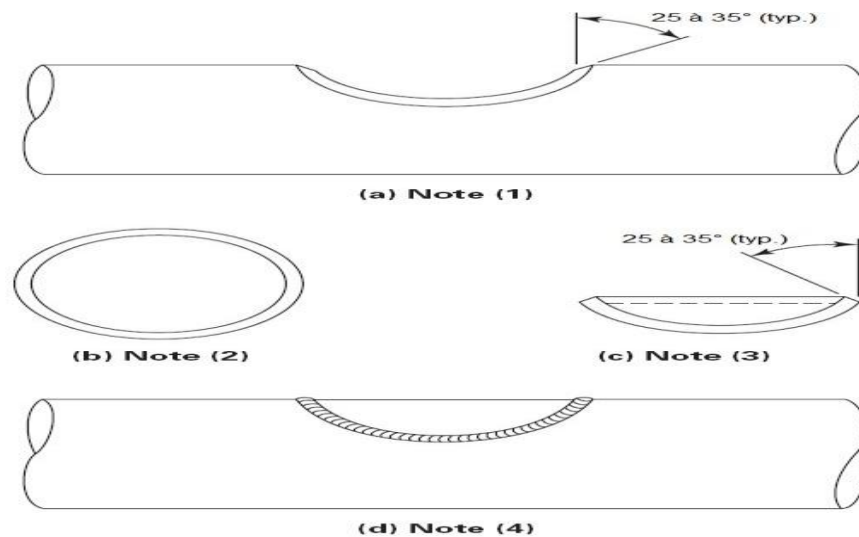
Type d'insertion d'une plaque soudée dans un tube
